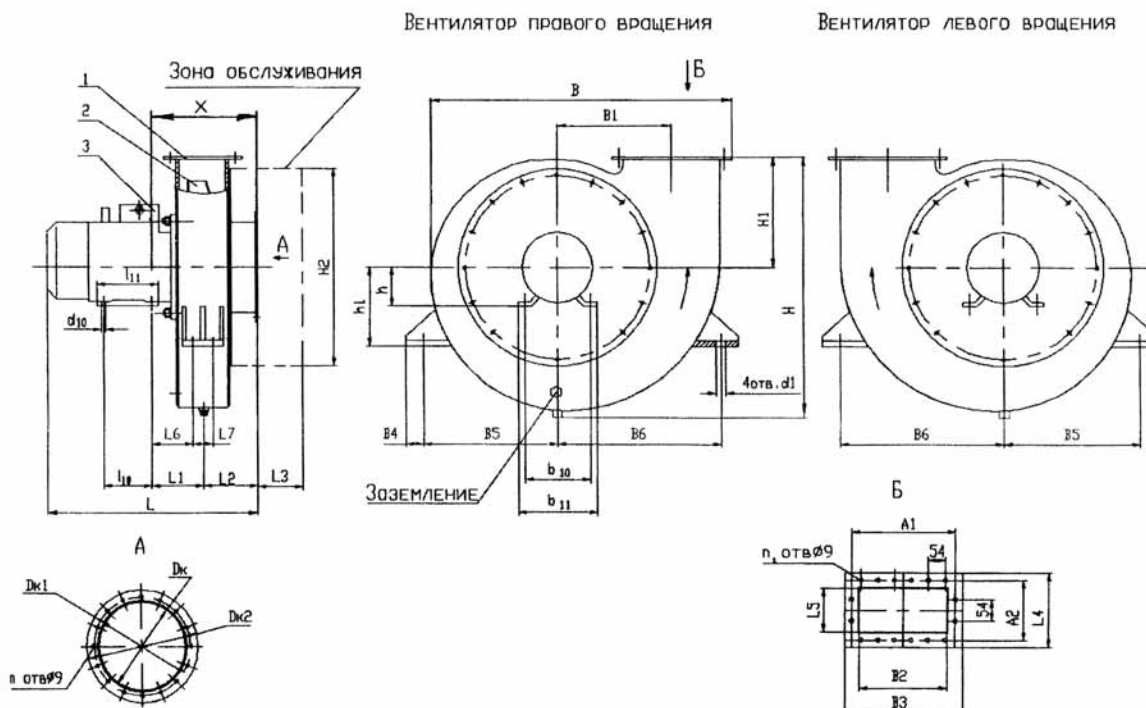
1 – корпус; 2 – колесо; 3 – двигатель
